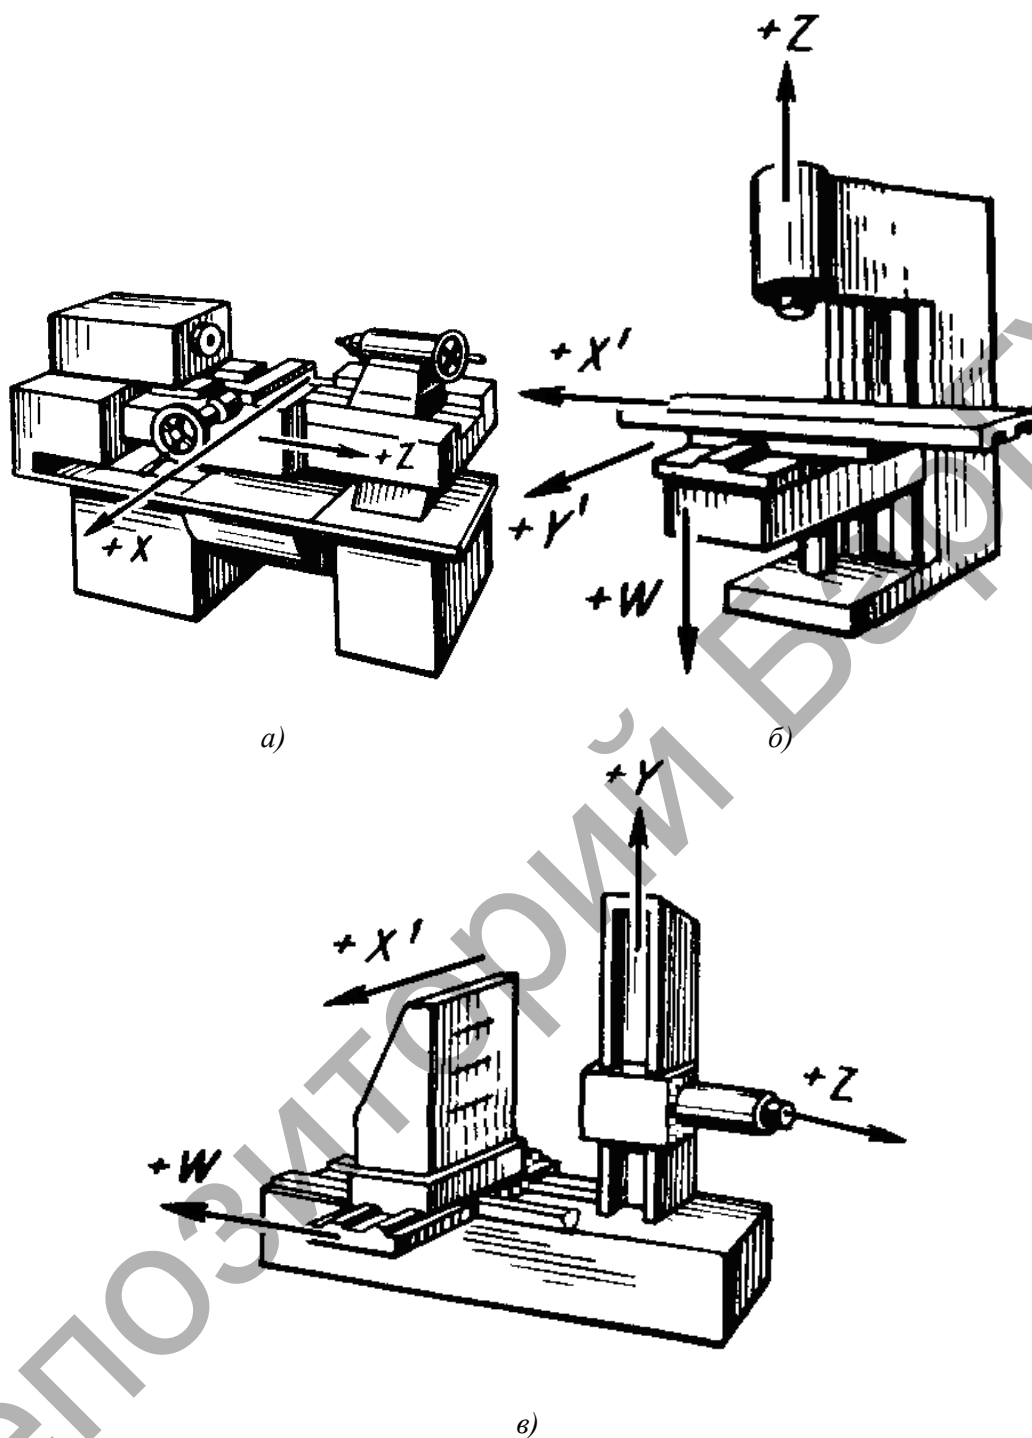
Обозначение движений инструмента и расположение осей координат в станках с ЧПУ
